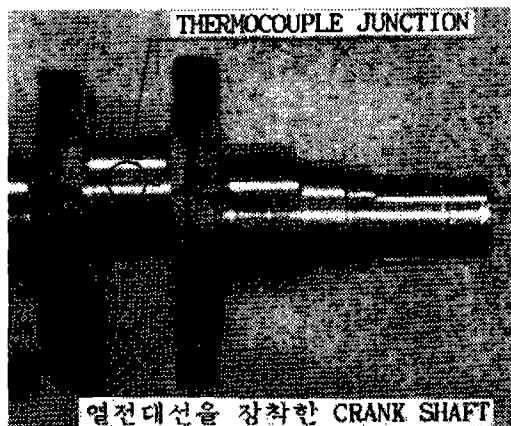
온도 측정에 사용된 엔진 및 Crank Shaft
